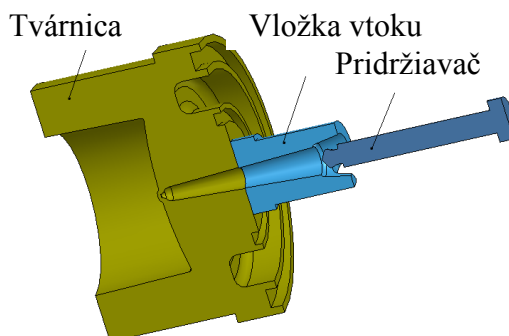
Systém rozvádzacích kanálov SolidWorks
